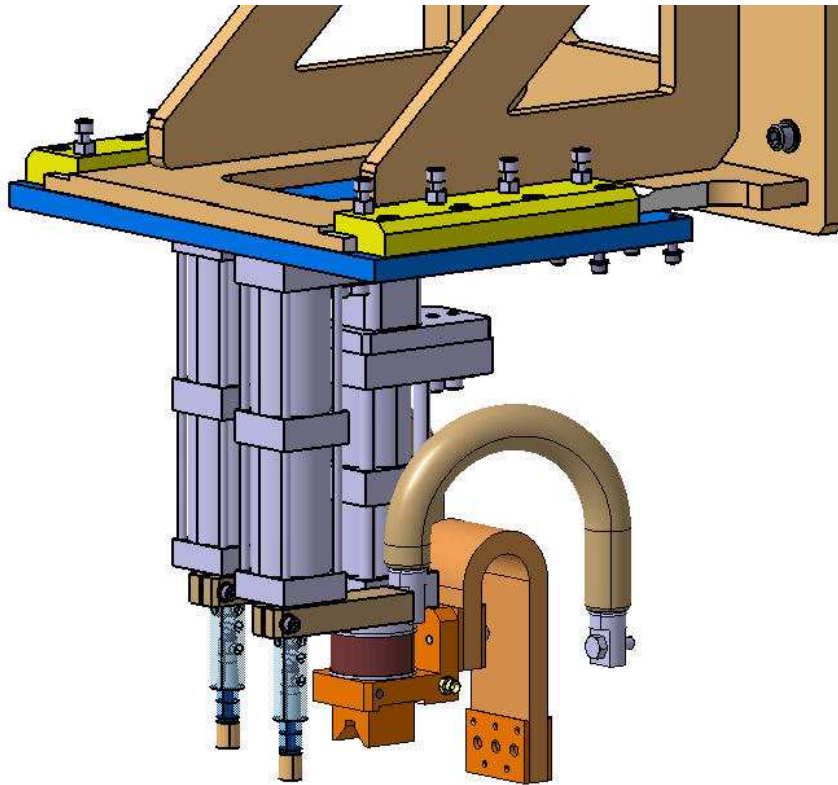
Conjunto de electrodos montados sobre cilindros de soldadura y cilindro de masa.
